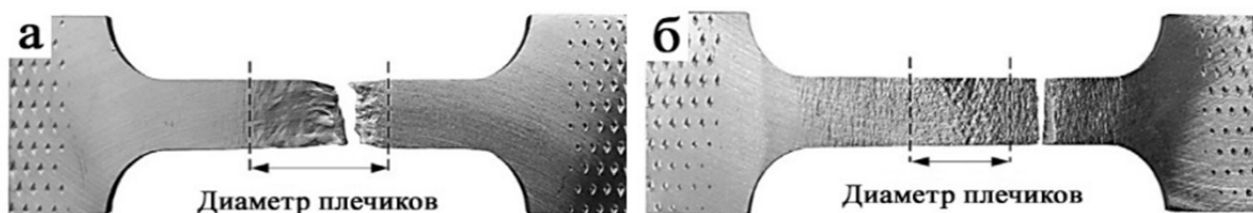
Внешний вид образцов, вырезанных из сварных соединений и разрушенных в ходе испытаний на одноосное растяжение после: (а) перезакалки и искусственного старения, (б) прокатки вдоль направления сварки на 10% с последующей перезакалки и старения
